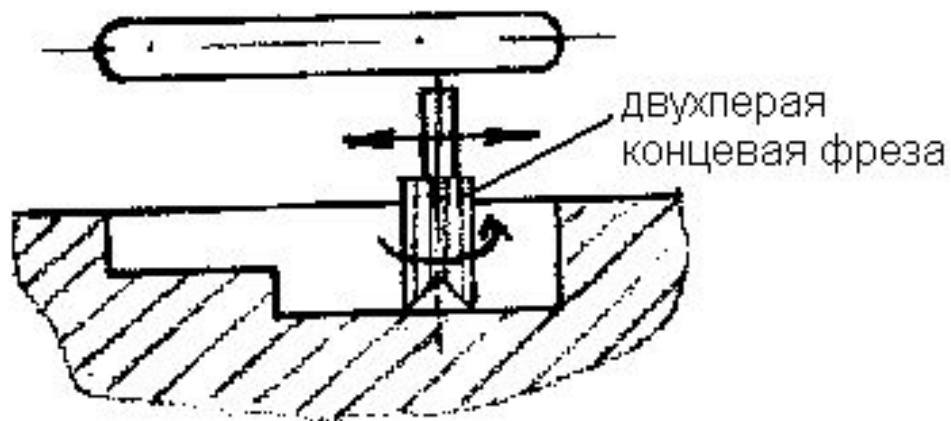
Нарезание шпоночного паза двухперой концевой фрезой
